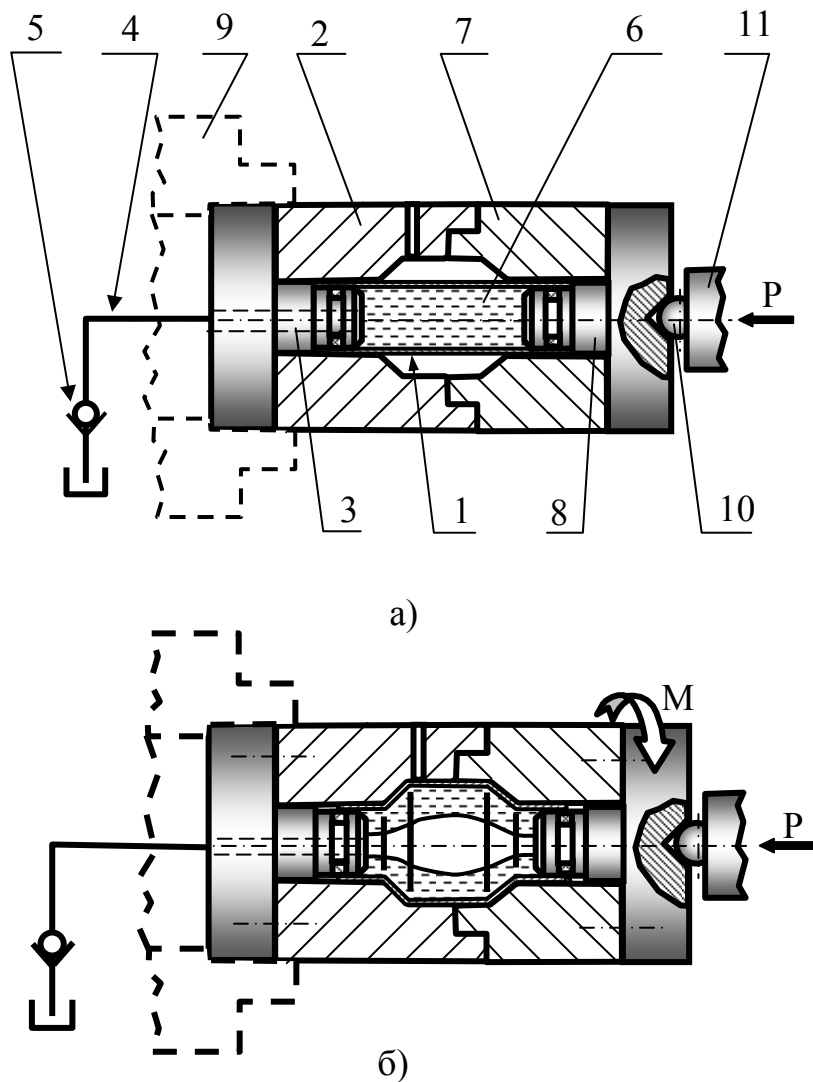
Начальный (а) и конечный (б) этапы инерционной раздачи трубной заготовки
